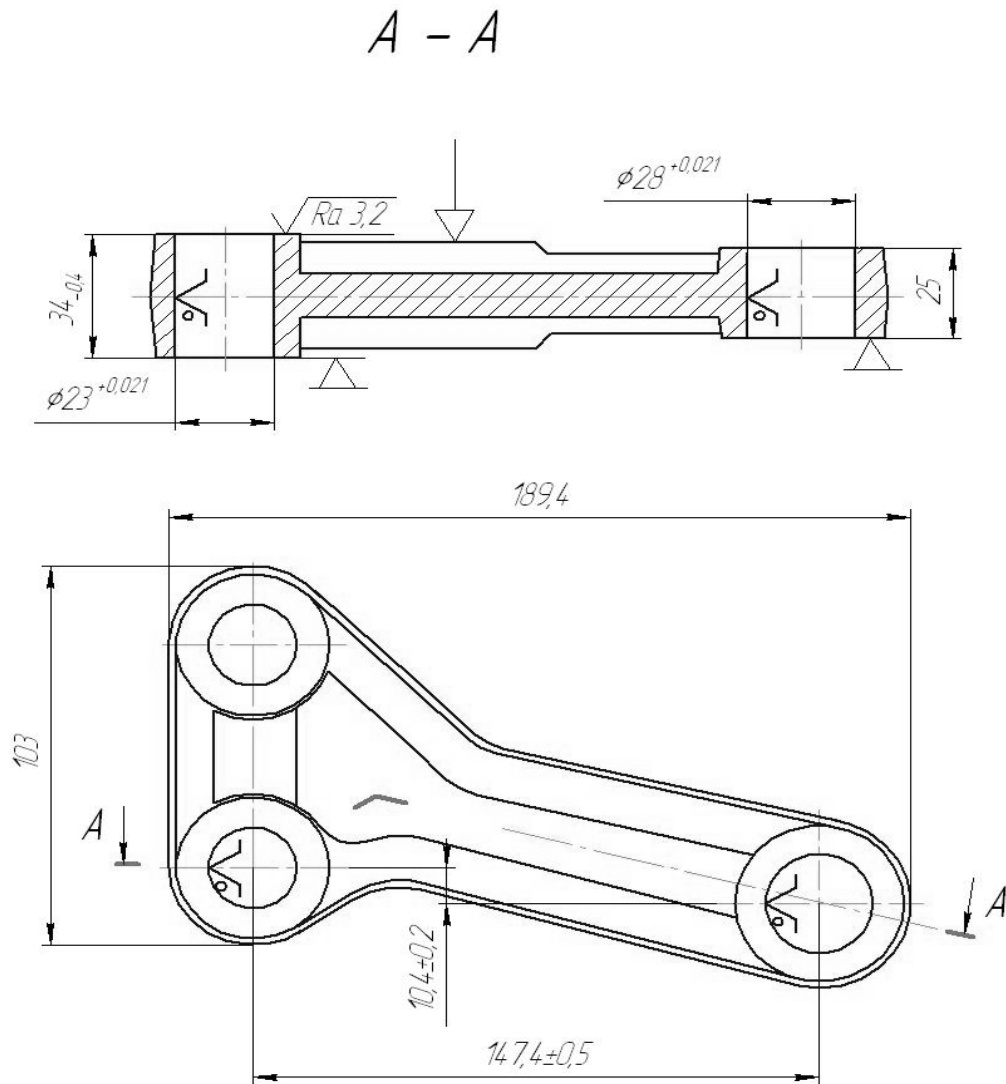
Схема базування важеля на фрезерному пристосуванні
